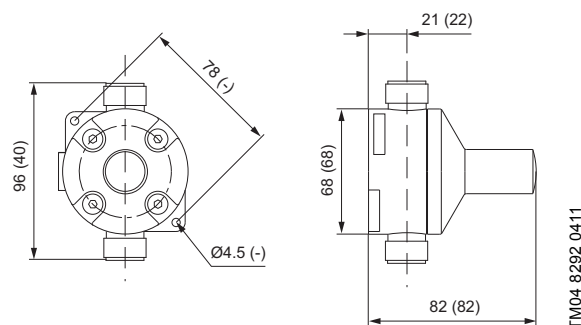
Druckhalteventil. Die Abmessungen in Klammern gelten für die Edelstahl-Version.
